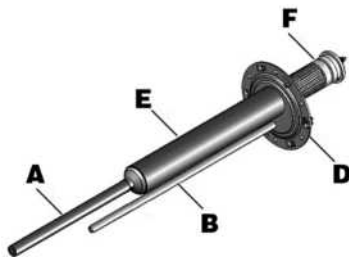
Стеатитовый нагревательный элемент + магниевый анод
